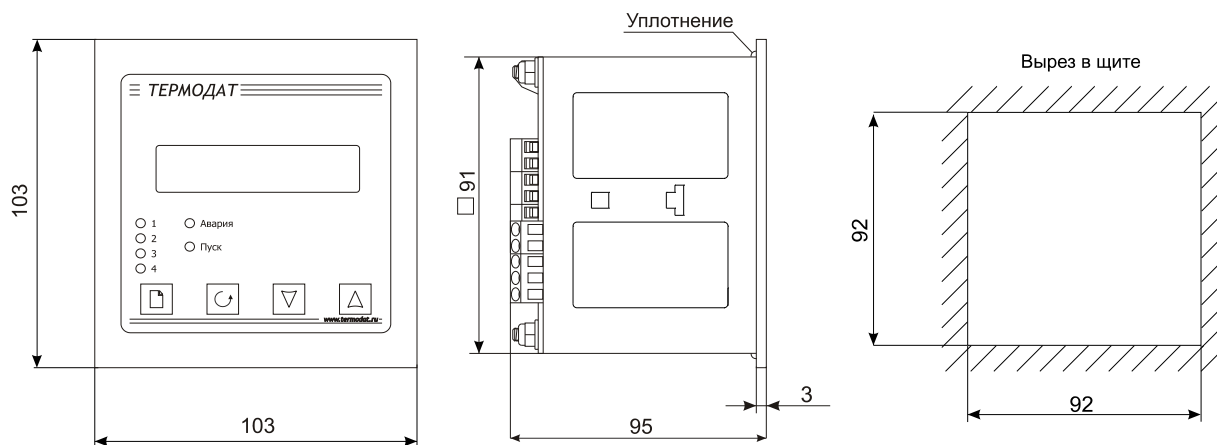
Габаритные размеры прибора Термодат-14Е5/...../IP67пп
